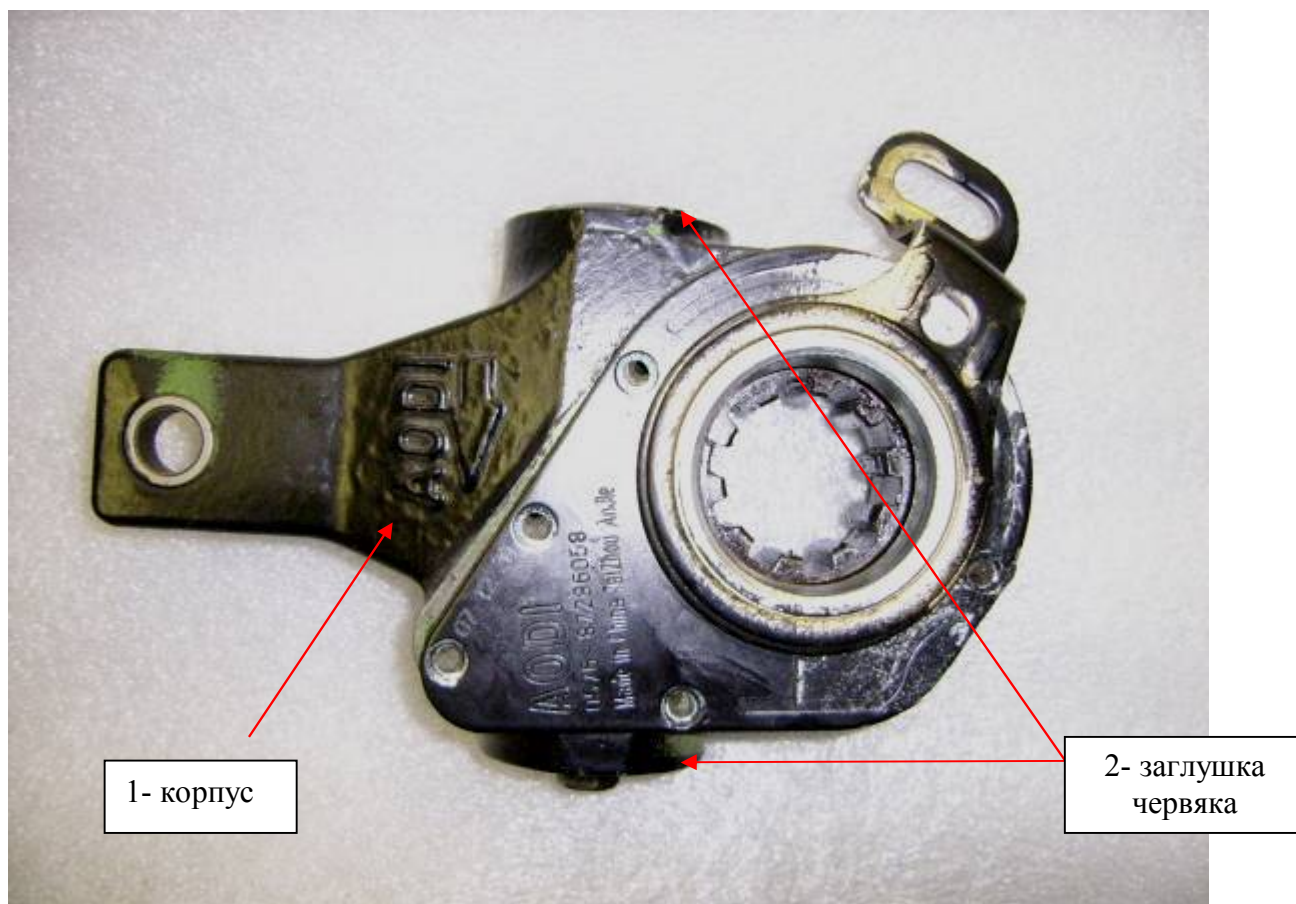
Вид сверху на механизм автоматической регулировки зазора
